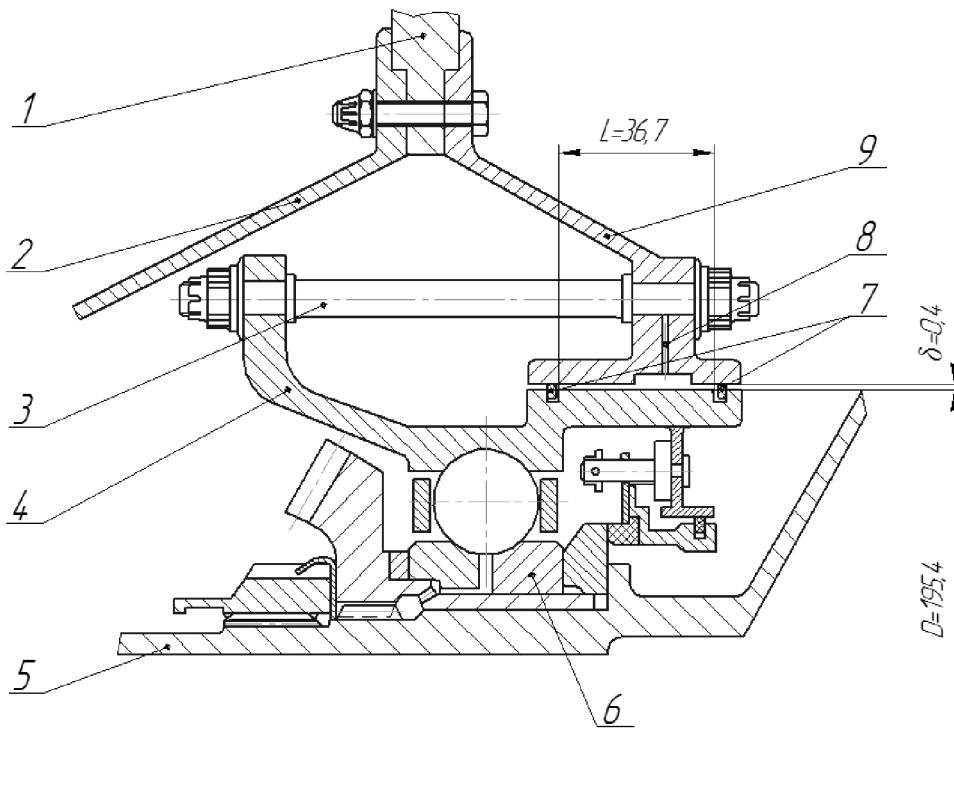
ГДД РУП КВД двигателя PW 6000
